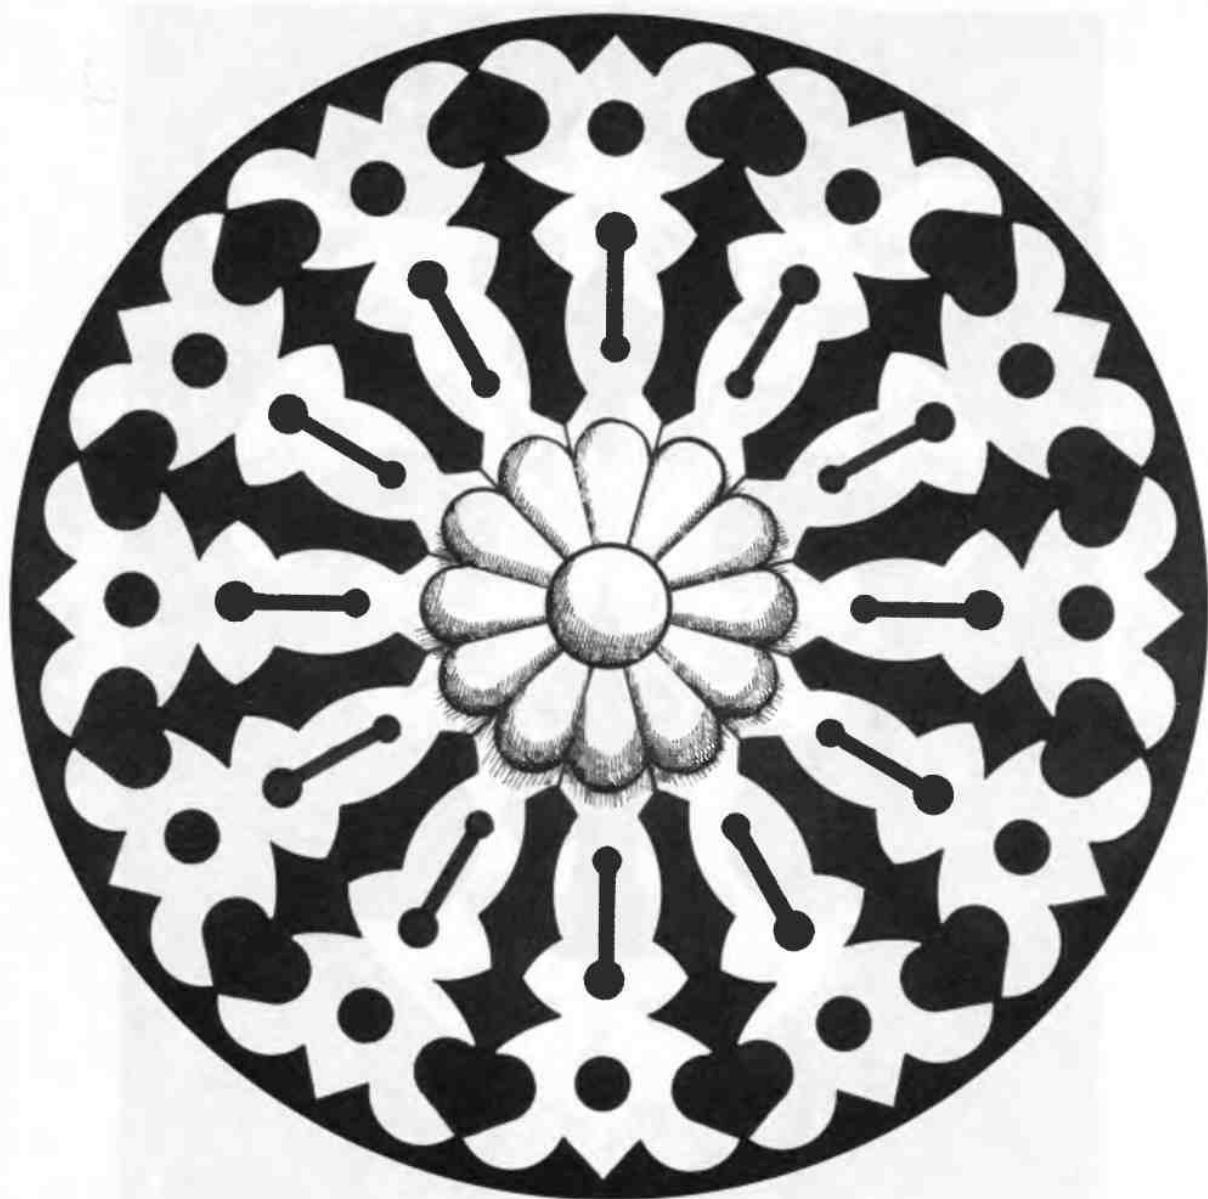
Вариант розетки для исполнения простыми инструментами: сверлами, обычной ножовкой и ножом (без выкружного лобзика)
